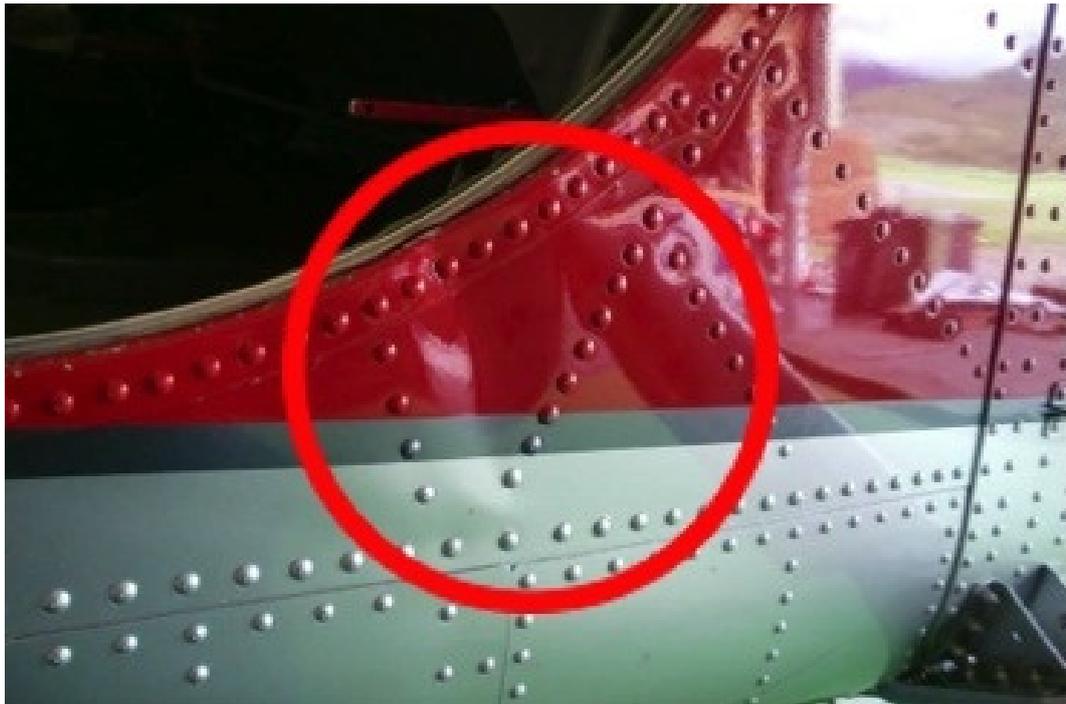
Déformations du fuselage sous l'encadrement extérieur de la porte avant gauche
